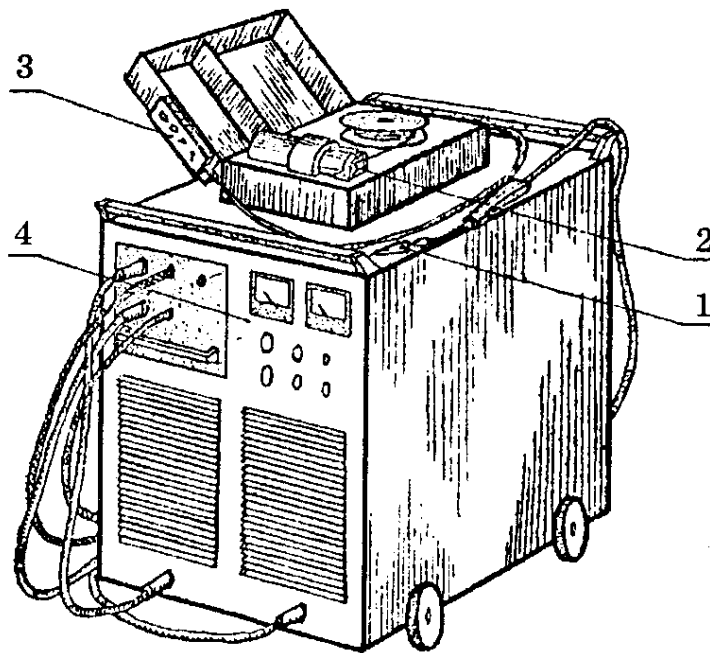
Сварочный полуавтомат ПДГ-305
